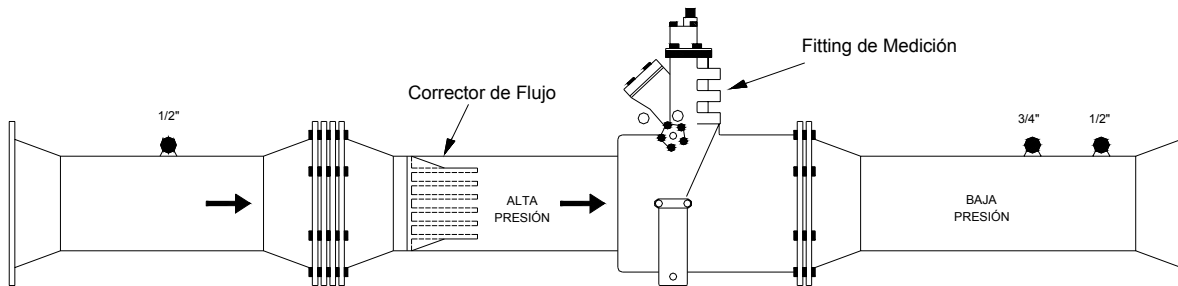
Tubo de medición de tres secciones con fitting flangeck y corrector de flujo, extremos biselados.
